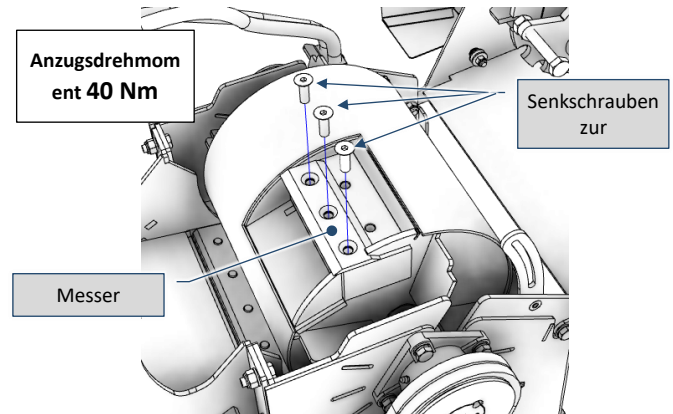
Detail der Senkschrauben zur Messerbefestigung
